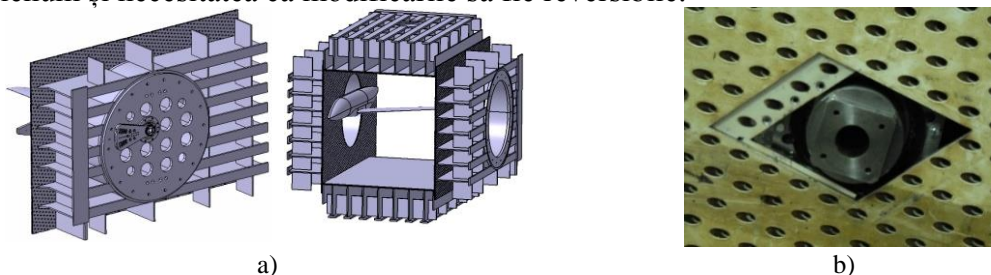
Adaptorul machetei montat la camera transonică a tunelului a), axul adaptorului cu flanșa pătrată; orificiul de transfer cablaj și tubulatura b)
